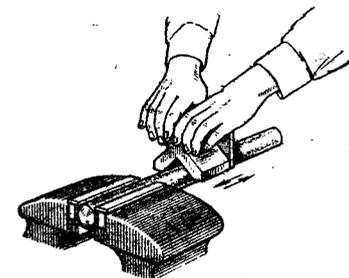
Прием притирки вогнутой поверхности радиусного шаблона
